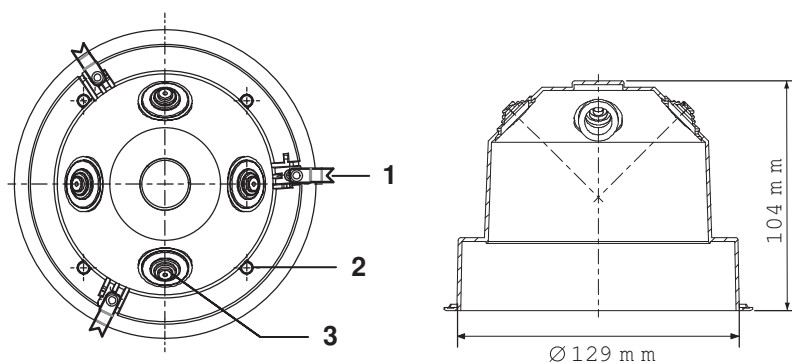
Вид сверху и сбоку корпуса для монтажа в потолок FAA-500-BB
